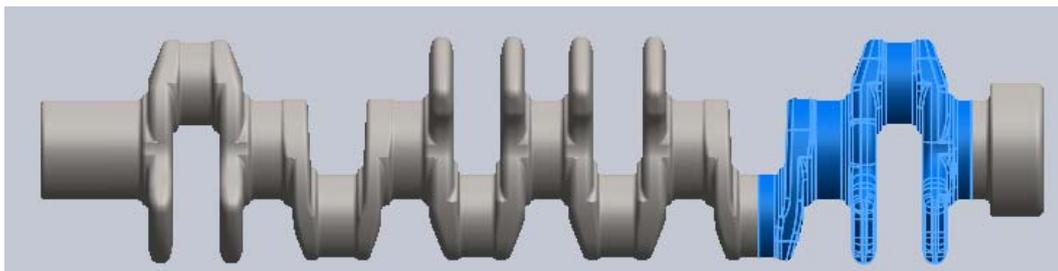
Выделение четвёртой части из детали коленчатого вала
